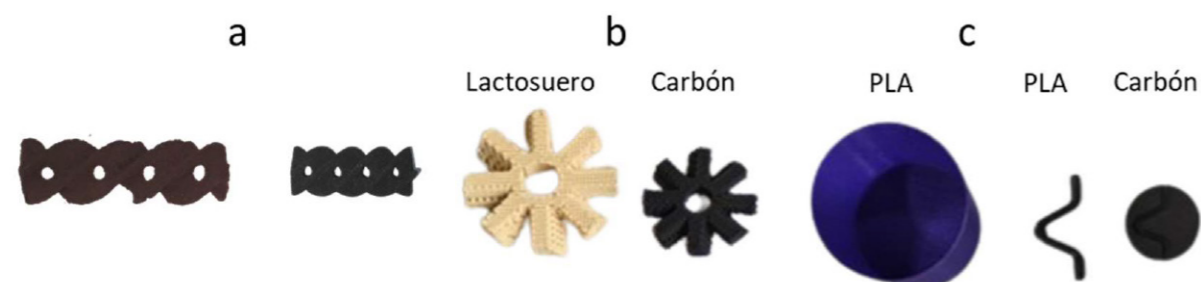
a) Pieza extraída de la máquina SLS (izquierda), pieza carbonizada SLS (derecha); b) pieza obtenida por DIW (izquierda), la misma pieza carbonizada (derecha), c) molde y modelo (izquierda y centro de la imagen), resultado final de la técnica PLA perdido (derecha).
